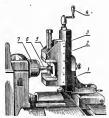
Универсальное приспособление для фрезерования мелких и средних деталей на токарном станке: 1 — литой угольник; 2 — поворотный суппорт; 3 — тиски; 4 — руконтка; 5 — обра-батываемое изделие; 6 — фреза; 7 — шинидель передней бабии
